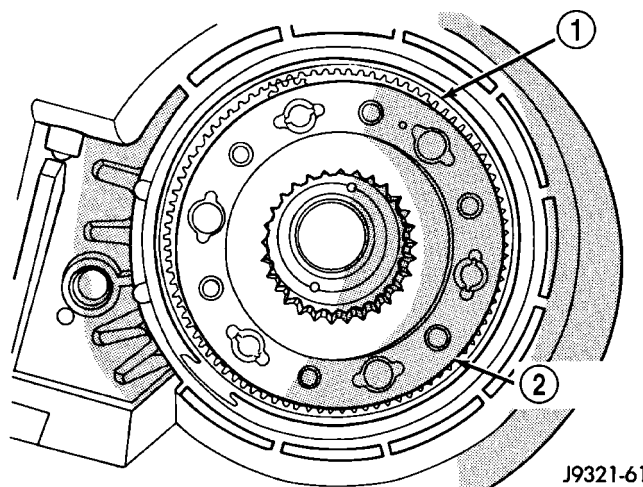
Instalación de los engranajes impulsor y de posición de baja
